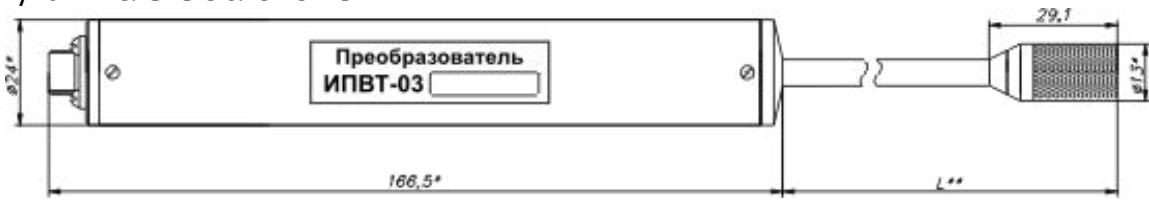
Измерительный преобразователь ИПВТ-03-04
